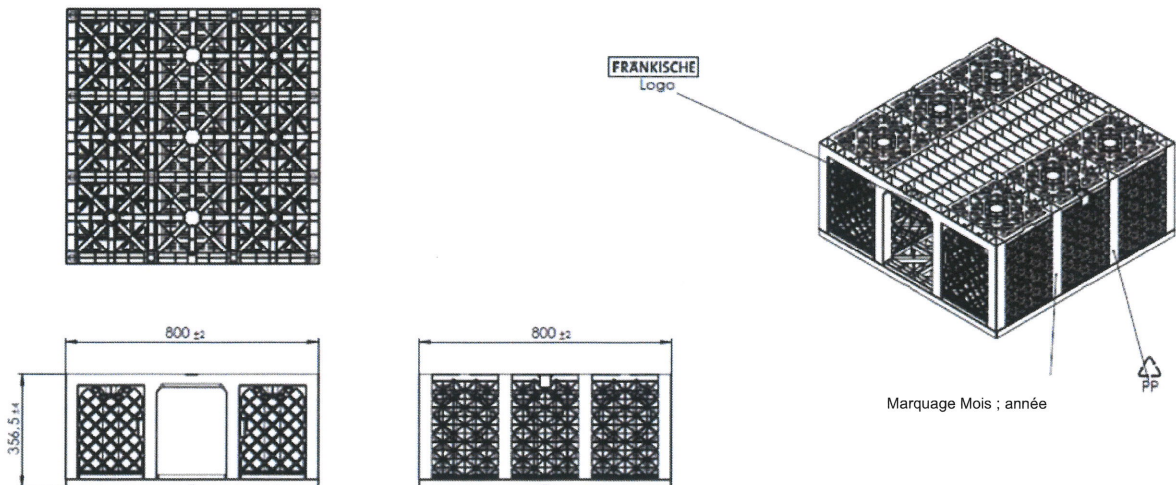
c- Caractéristiques dimensionnelles du demi-module Rigofill inspect
